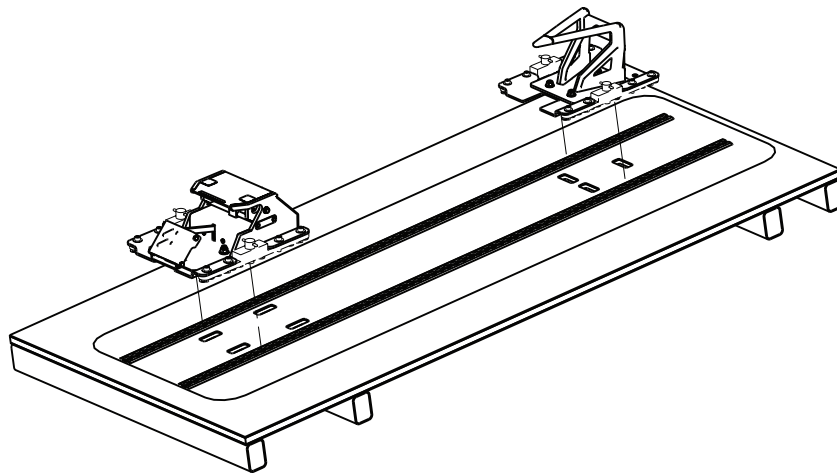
Fixations côté tête et côté pieds - installation sur le rail de plancher
